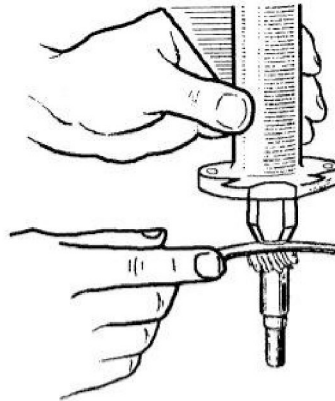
Проверка осевого зазора между корпусом привода масляного насоса и датчиком-распределителем зажигания с шестерней.
